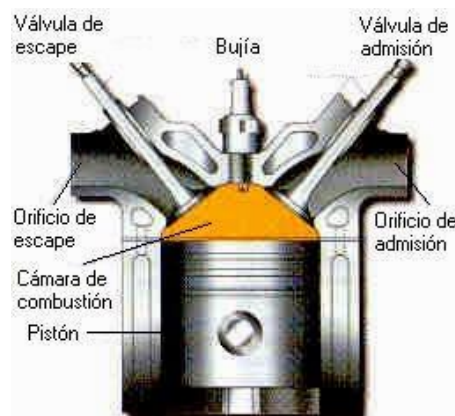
Partes de una cámara de combustión. Fuente: ELECTROMECAÁNICA [9]
